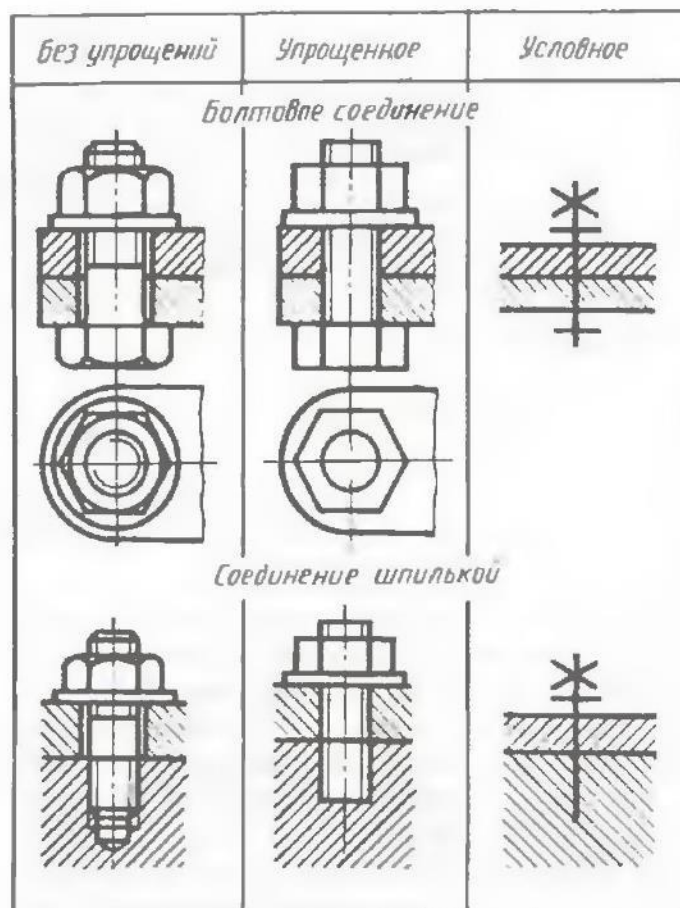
Резьбовое соединение болтом и шпилькой
